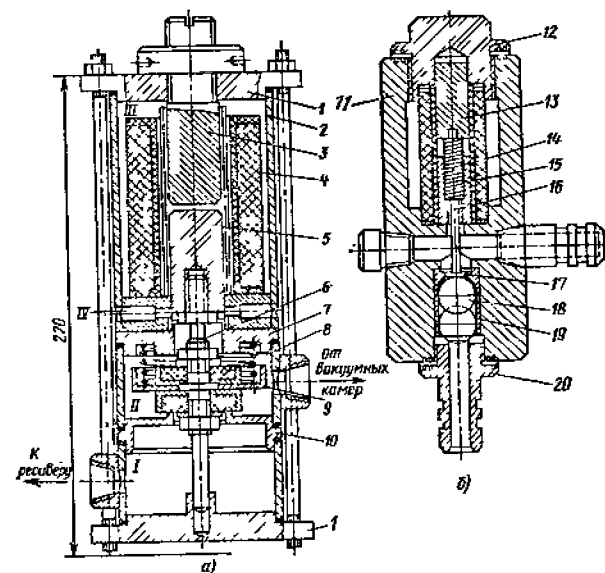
Вакуумные клапаны: а — двухходовой электромагнитный; б — противоподсосный клапан
